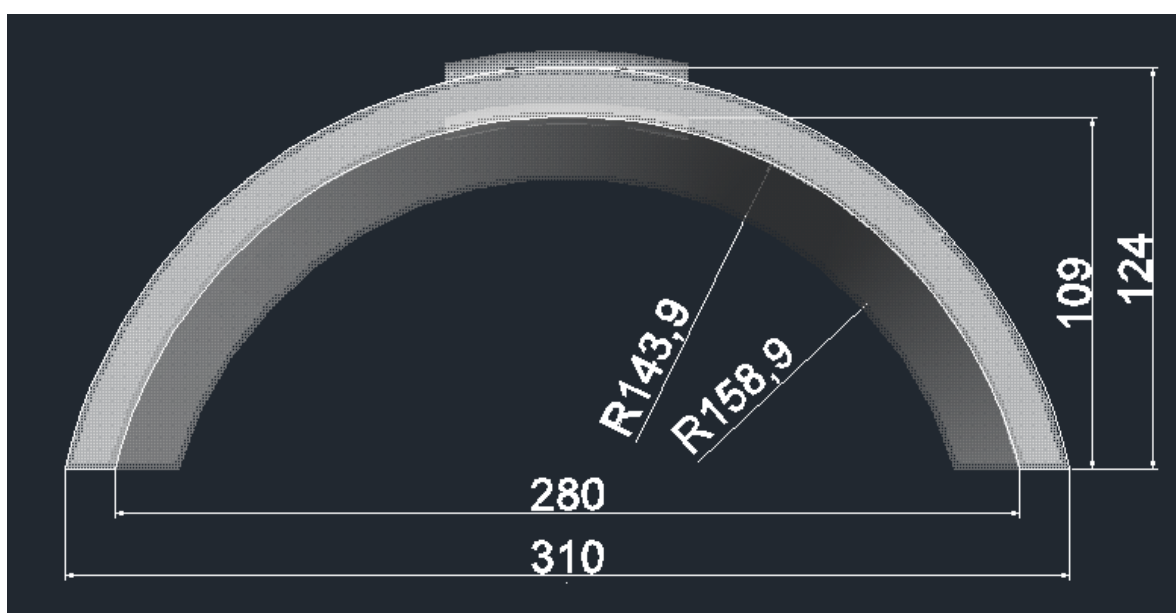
Dimensões da lateral de maior raio da telha GePET.
